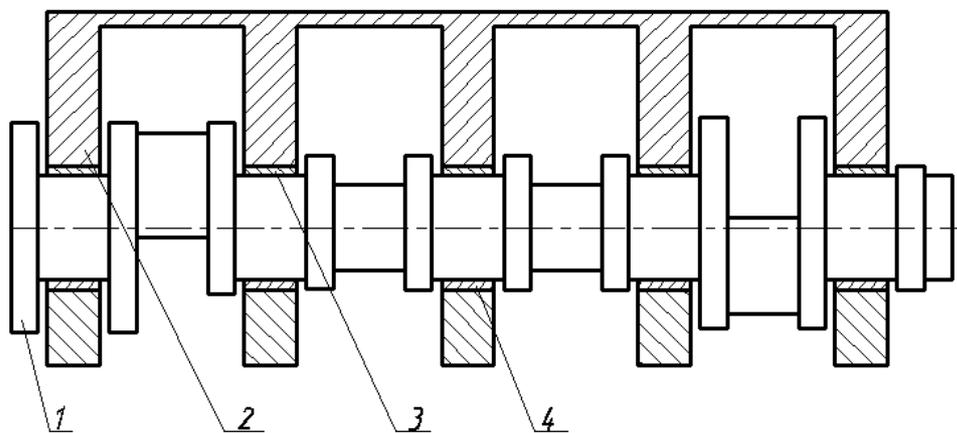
Схема многоопорного узла поддержки коленчатого вала: 1 – коленчатый вал, 2 – картер, 3 – верхний коренной вкладыш, 4 – нижний коренной вкладыш
